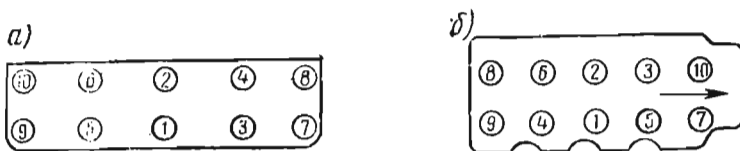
Последовательность подтяжки гаек крепления головки цилиндров двигателей:
